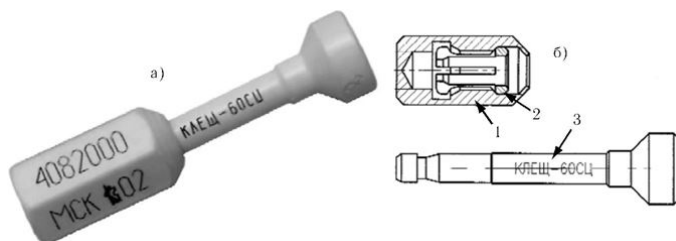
Общий вид ЗПУ «Клещ-60СЦ» (а); конструкция запирающего механизма в разрезе (б): 1 — корпус, 2 — цанга, 3 — стержень;
